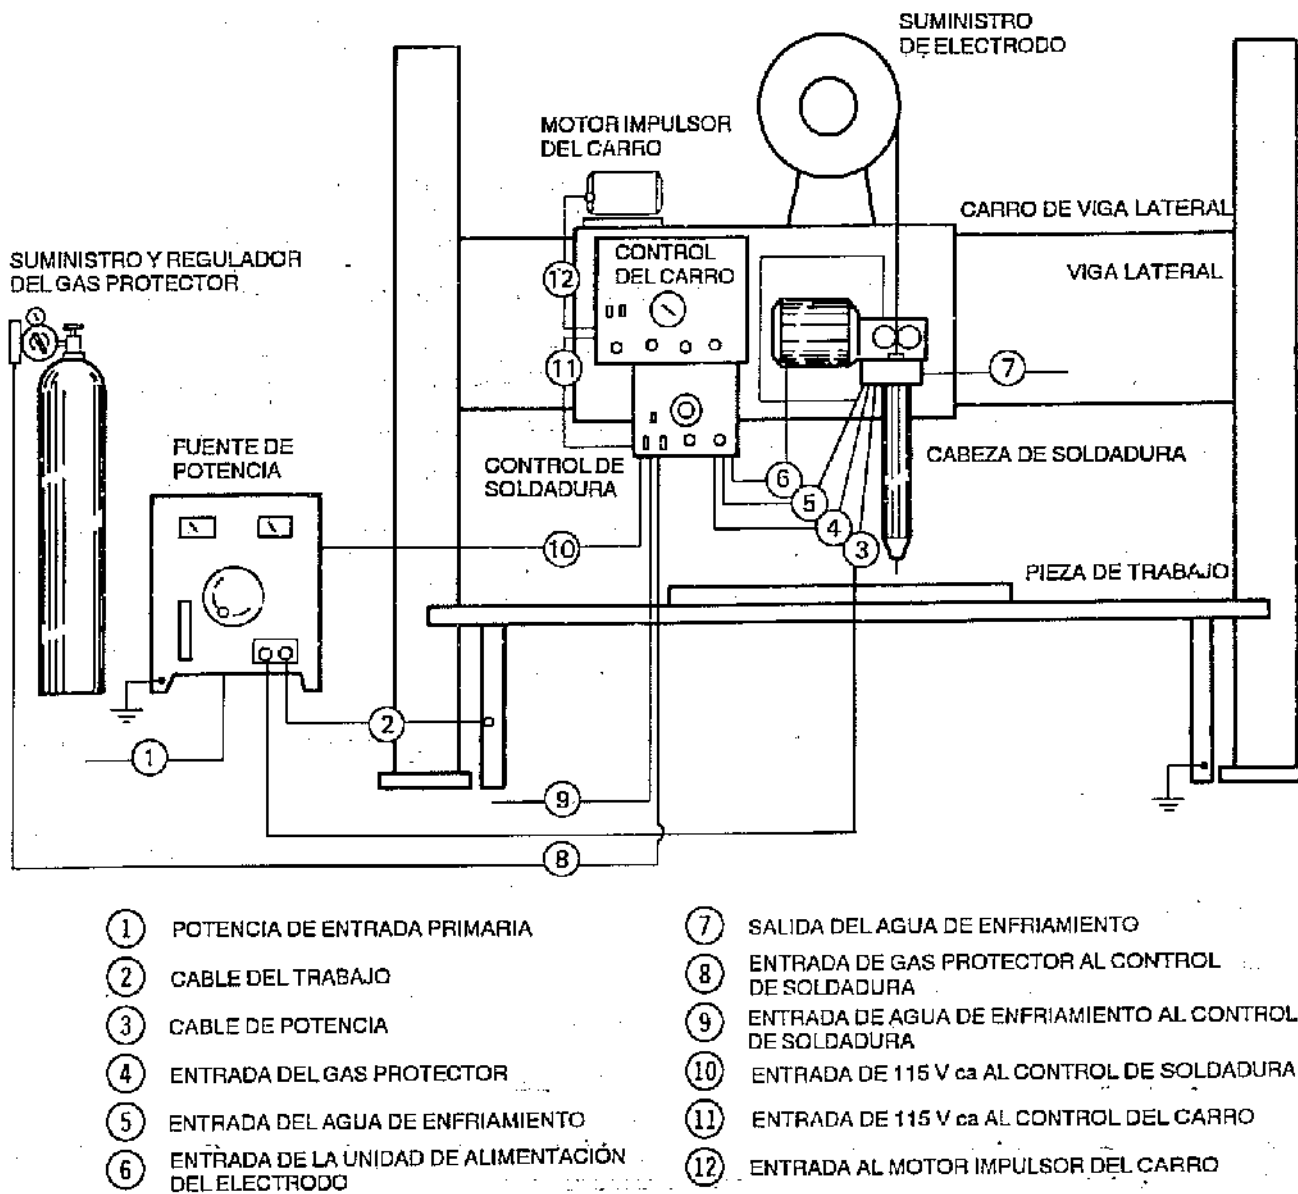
Instalación para soldadura por arco de metal y gas mecanizada
